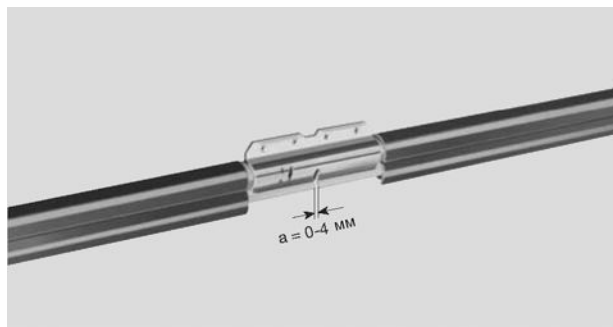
Рельсовое соединение UV 10 без закрывающего колпачка
